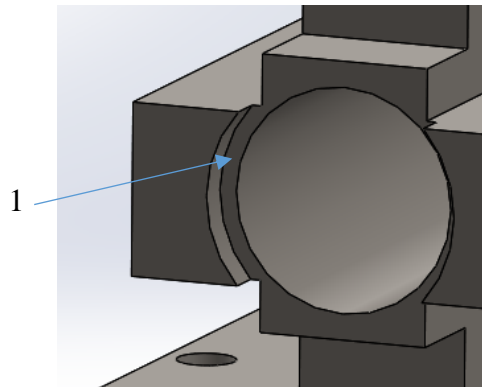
Pormenor do núcleo final; 1) rebaixo
